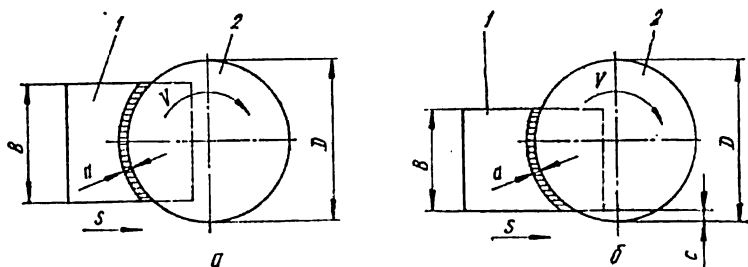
Схемы резания торцовой фрезой при фрезеровании: а — симметрично; б — несимметрично.
